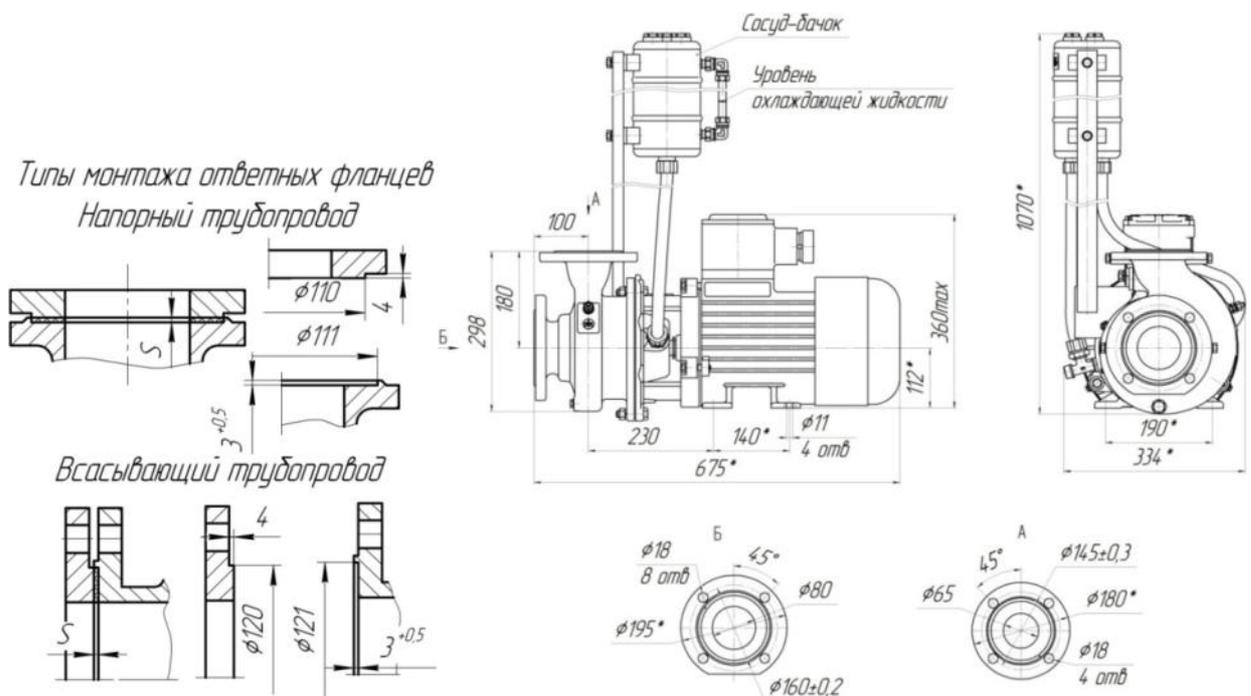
Габаритные и присоединительные размеры КМ 80-65-160Е(а,б)-м с двойным торцовым уплотнением
